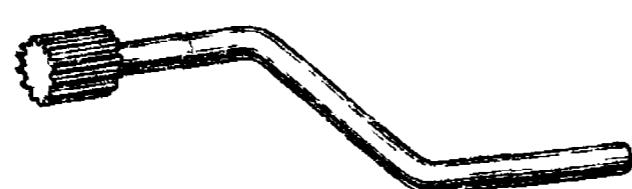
Рукоятка для проворачивания коленчатого вала двигателя
